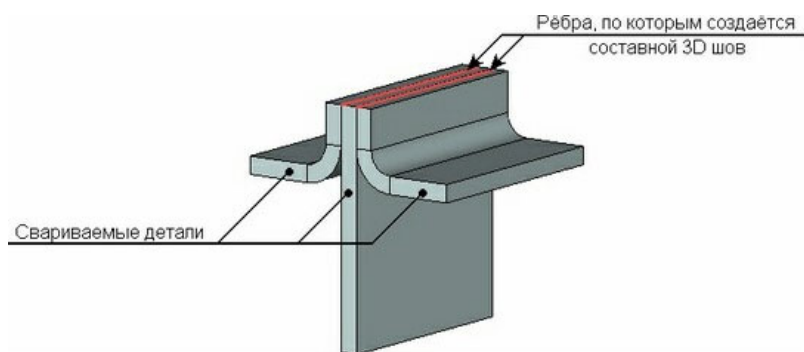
Создание сварного шва по рёбрам
